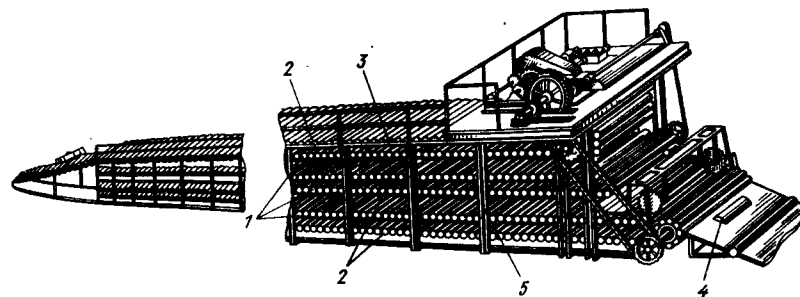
Общий вид конвейера для твердения трехметровых труб:
